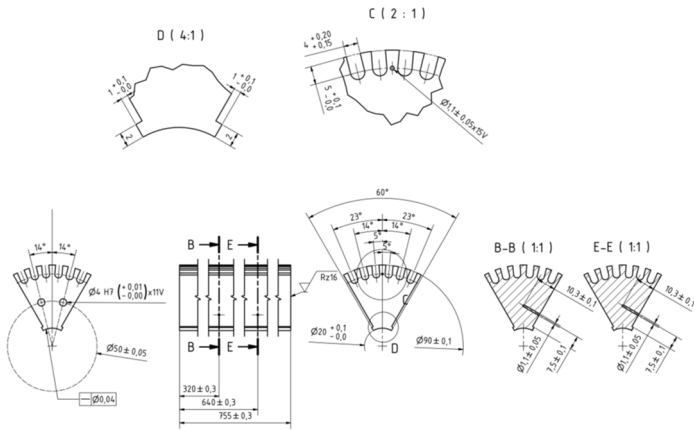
Technische Zeichnung eines Heizsegments der Messstrecke mit Bohrungen für die Thermoelementplatzierung.
